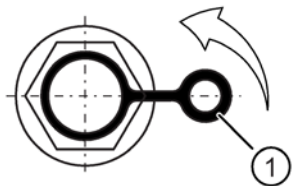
Druckentlüftungsventil mit Sicherungsglasche
